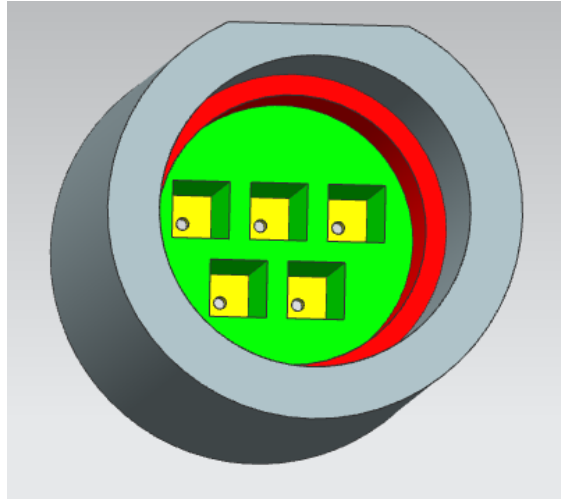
2º diseño de la pieza de encaje entre base y tubo utilizando cables Dupont
